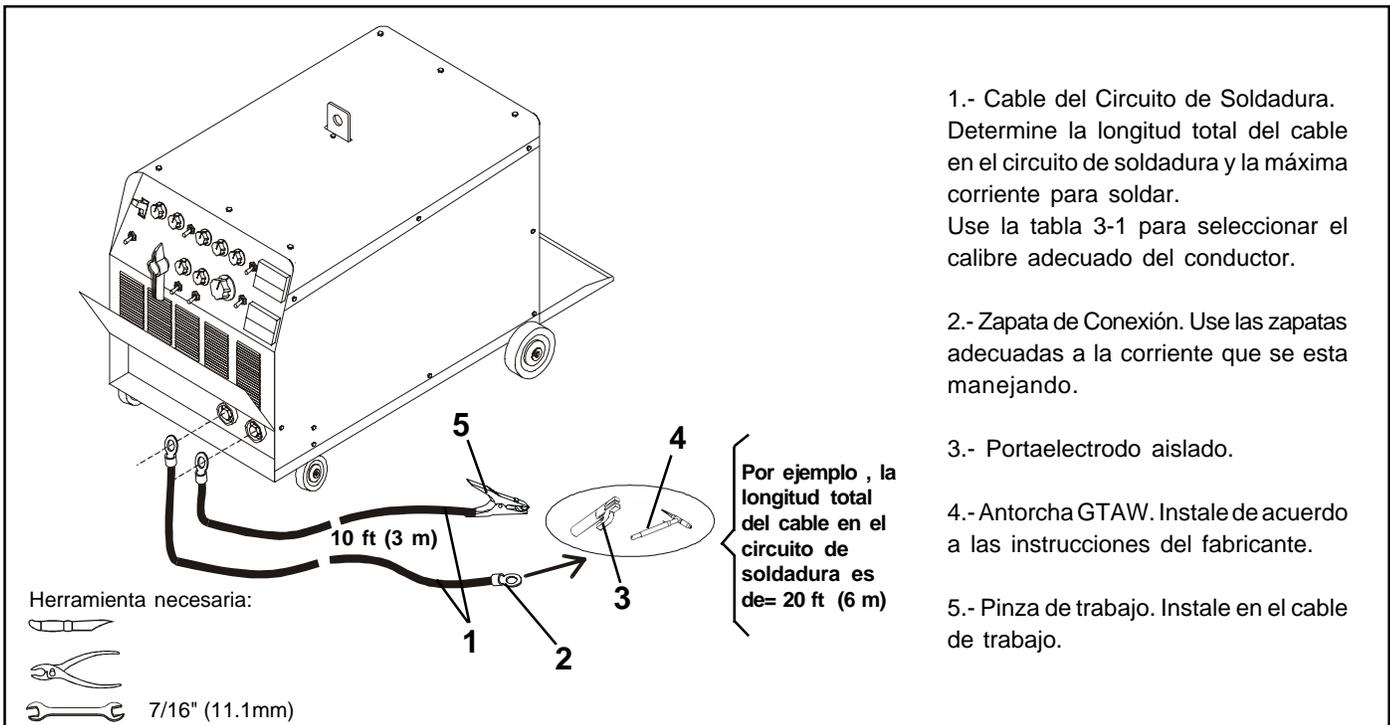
SELECCIÓN DE LOS CABLES PARA SOLDAR
